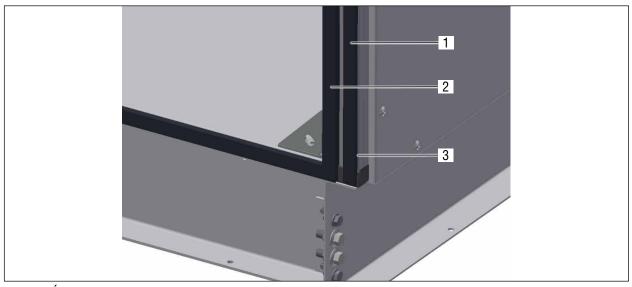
Étanchéité du point de séparation en cas d'installation extérieure
